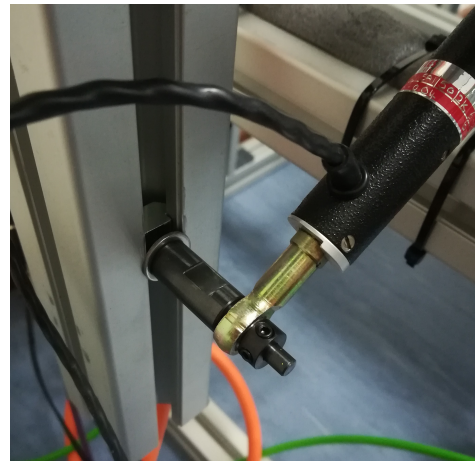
Pièce de fixation d'une extrémité d'un capteur - Assemblée
